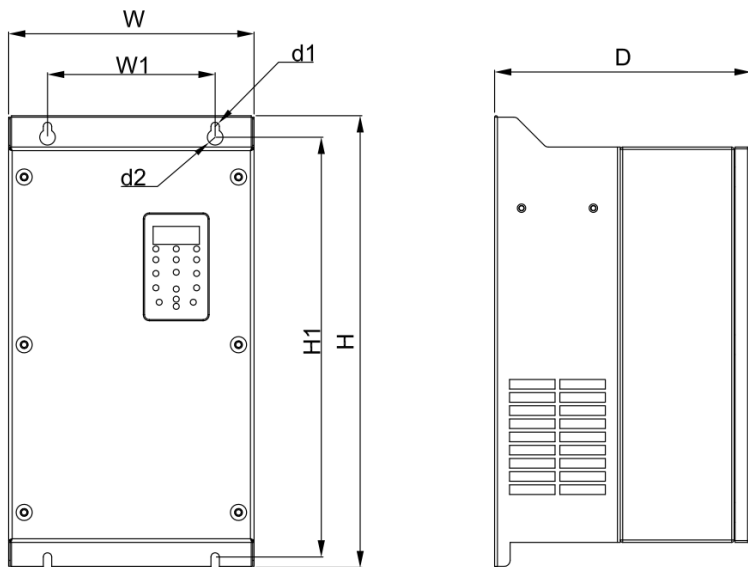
0,7~22 кВт Схема настенного монтажа
